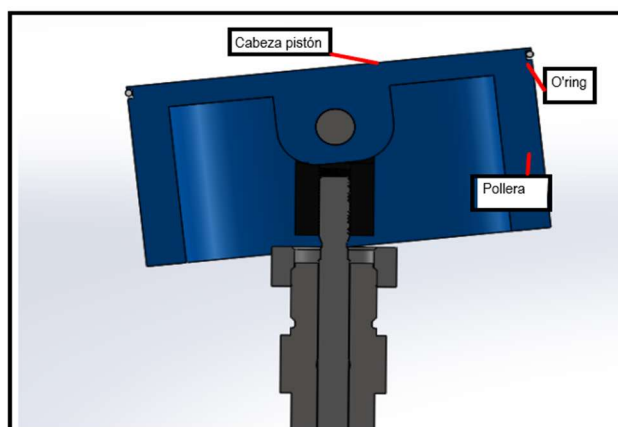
Detalle de unión entre pistón y cilindro neumático
